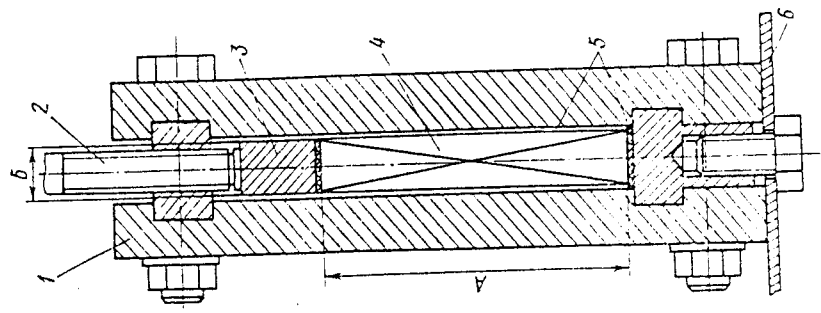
Пресс-форма для опрессовки пазовой части корпусной изоляции стержней
